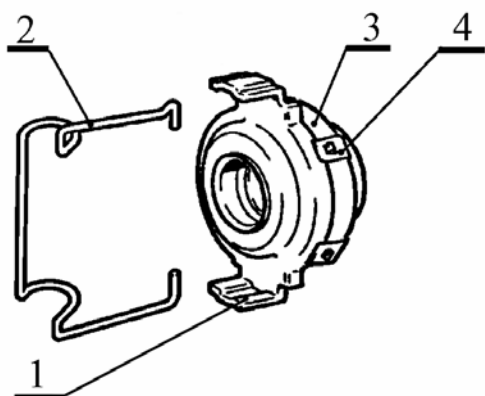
Детали муфты 2110-1601180 подшипника выключения сцепления в сборе:
